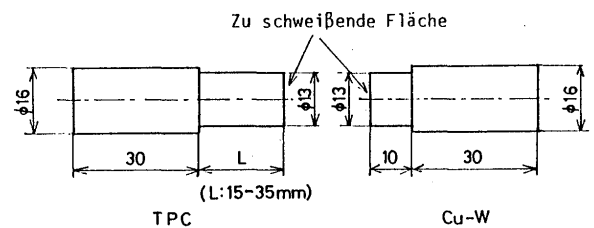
Abmessungen der Proben für Reibschweißen.
